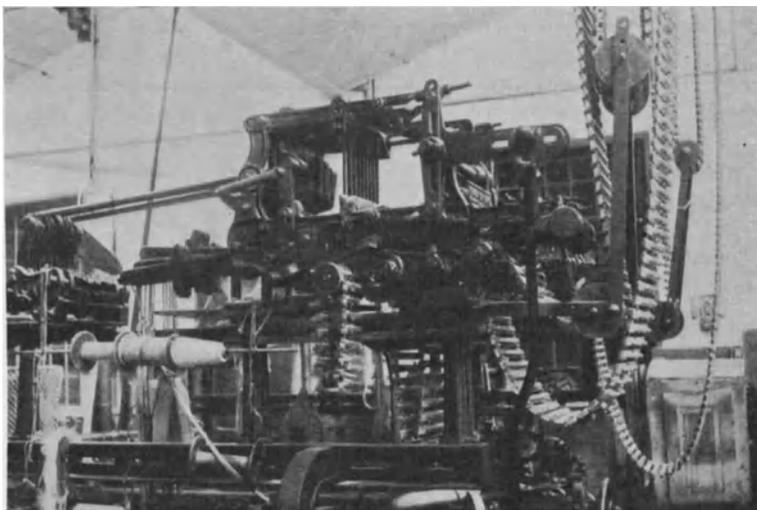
Webstuhl mit Schaftmaschine für Holzkarte, 2 Zylinder (Hinteransicht).
